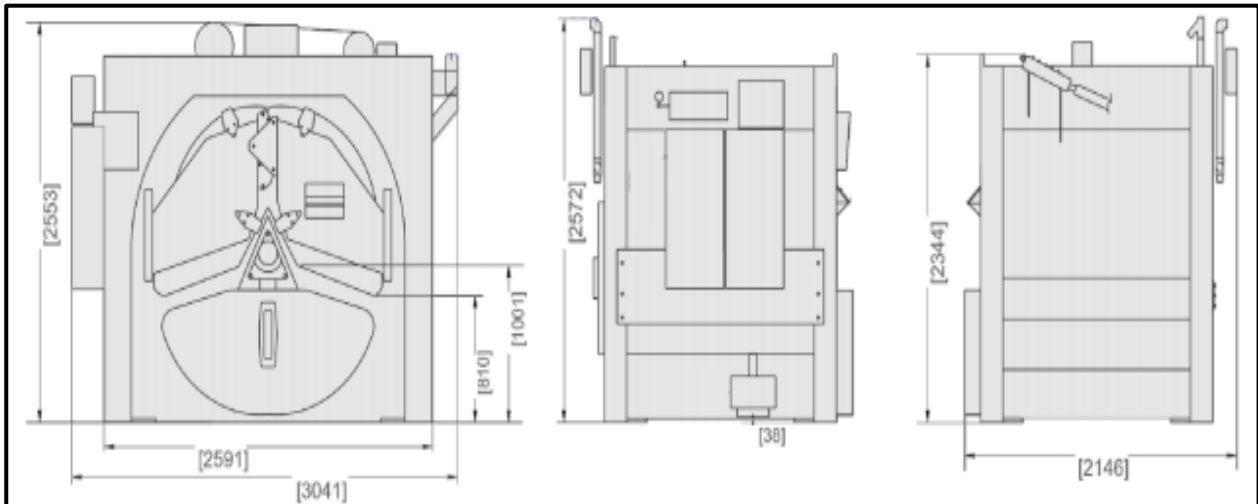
Dimensiones vista frente y laterales lavadora industrial Milnor-300 (mm).
